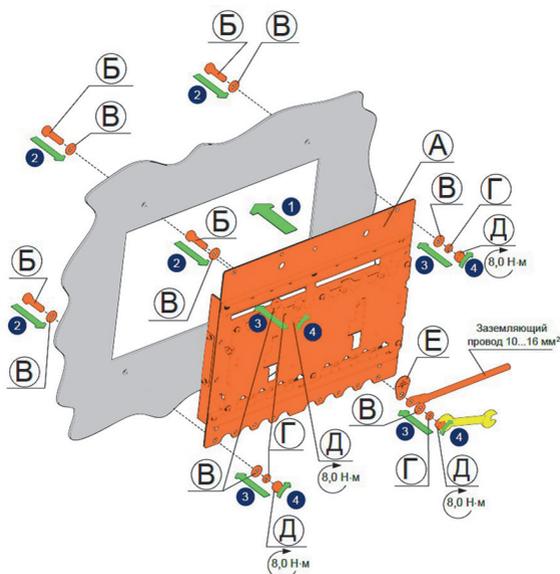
Установка рамы механической блокировки на панель для установки стационарных выключателей
